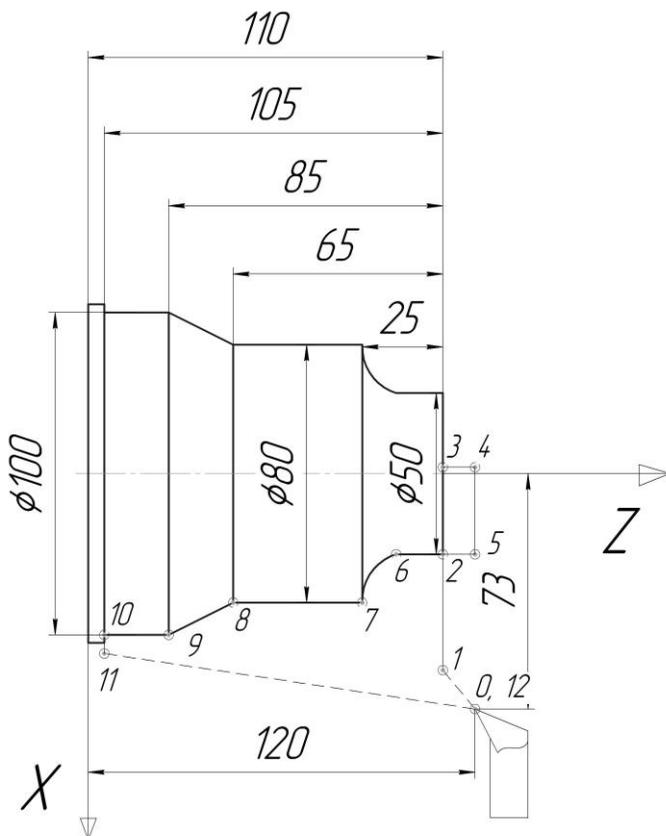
Пример эскиза детали с траекторией движения инструмента и осями координат станка
